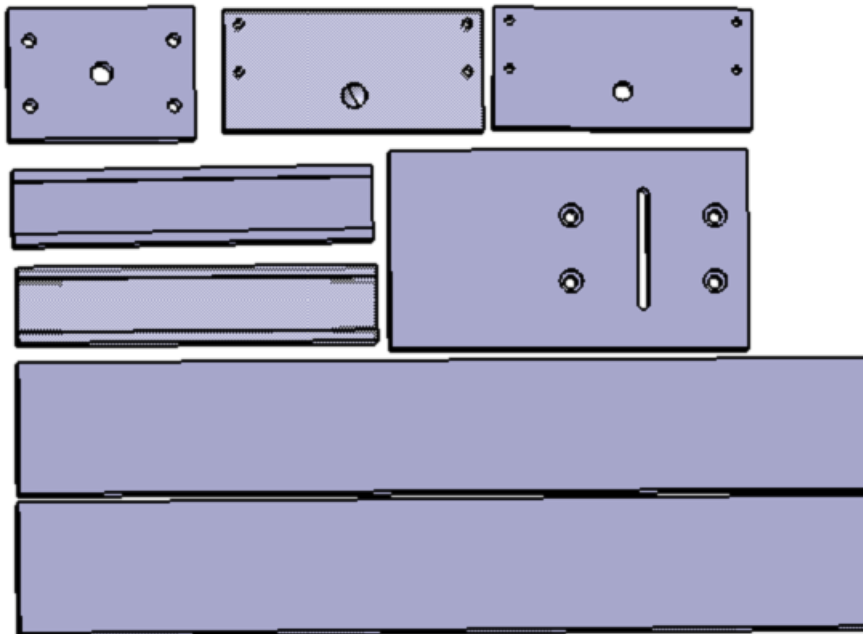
Plano de corte utilizado para las piezas de 20mm
